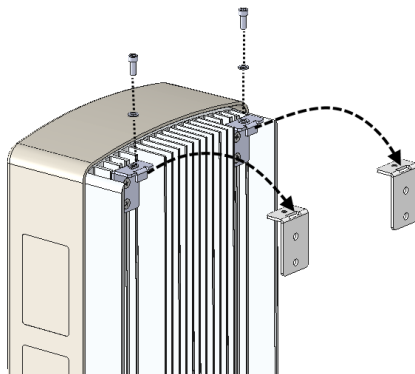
Fissaggio dell'inverter alle staffe - Tipo 1
